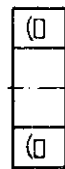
Роликовый подшипник упорно-радиальный однорядный (сферический)
